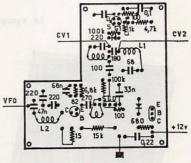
Le circuit imprimé du VFO (vue de dessous, côté cuivre)
